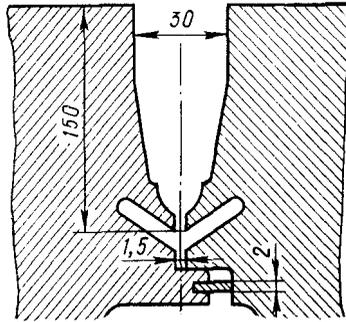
Конструкция стыка кольцевого соединения вала ротора турбины
